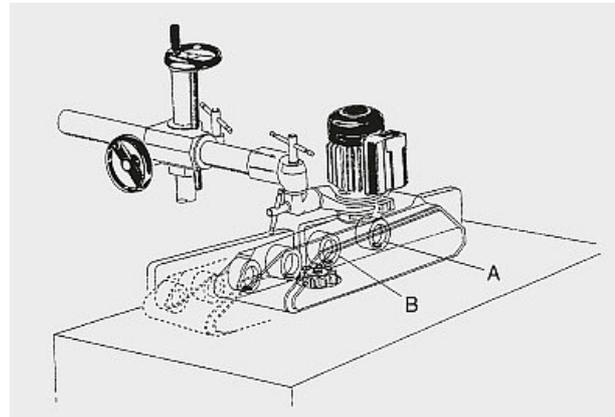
Anbringen an einer Tischfräsmaschine
